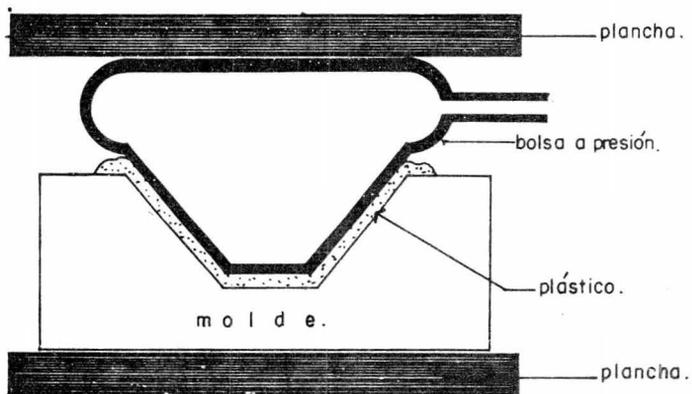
REFORZADO.- MOLDEO EN BOLSA A PRESION.
